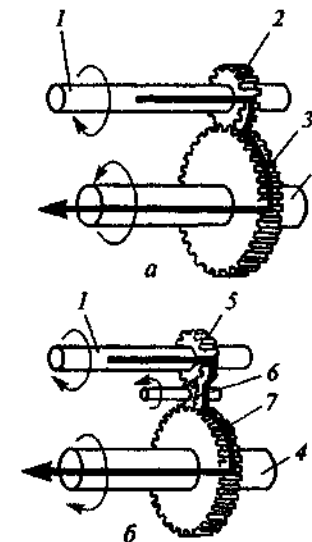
Схема работы двухвальной коробки передач: а — движение вперед, б — движение задним ходом; 1 — первичный вал; 2, 3, 5, 6 и 7 — шестерни; 4 — вторичный вал
